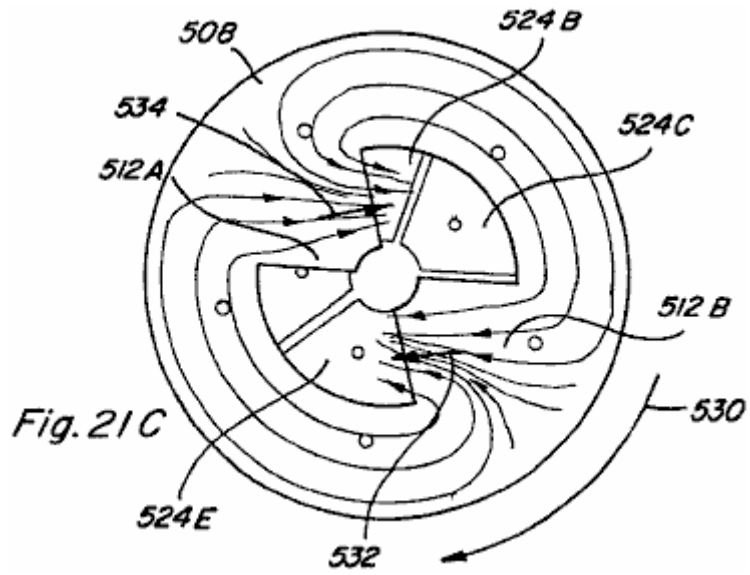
A-Fig.21E sind Draufsichten auf die teilweise Montage von Fig.20, die zeigen eine Drehbewegung desselben Ansichten,
